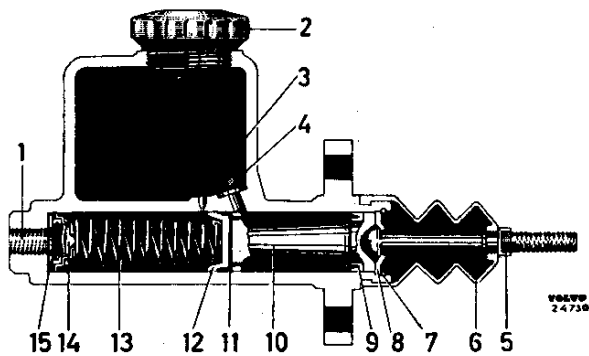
Hauptbremszylinder, spätere Ausführung.
